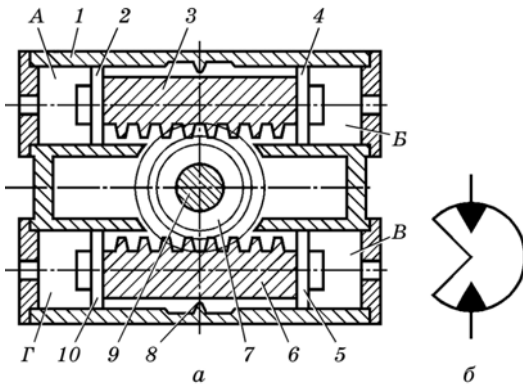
Схема чотирипоршневого дворейкового поворотного гідродвигуна:
